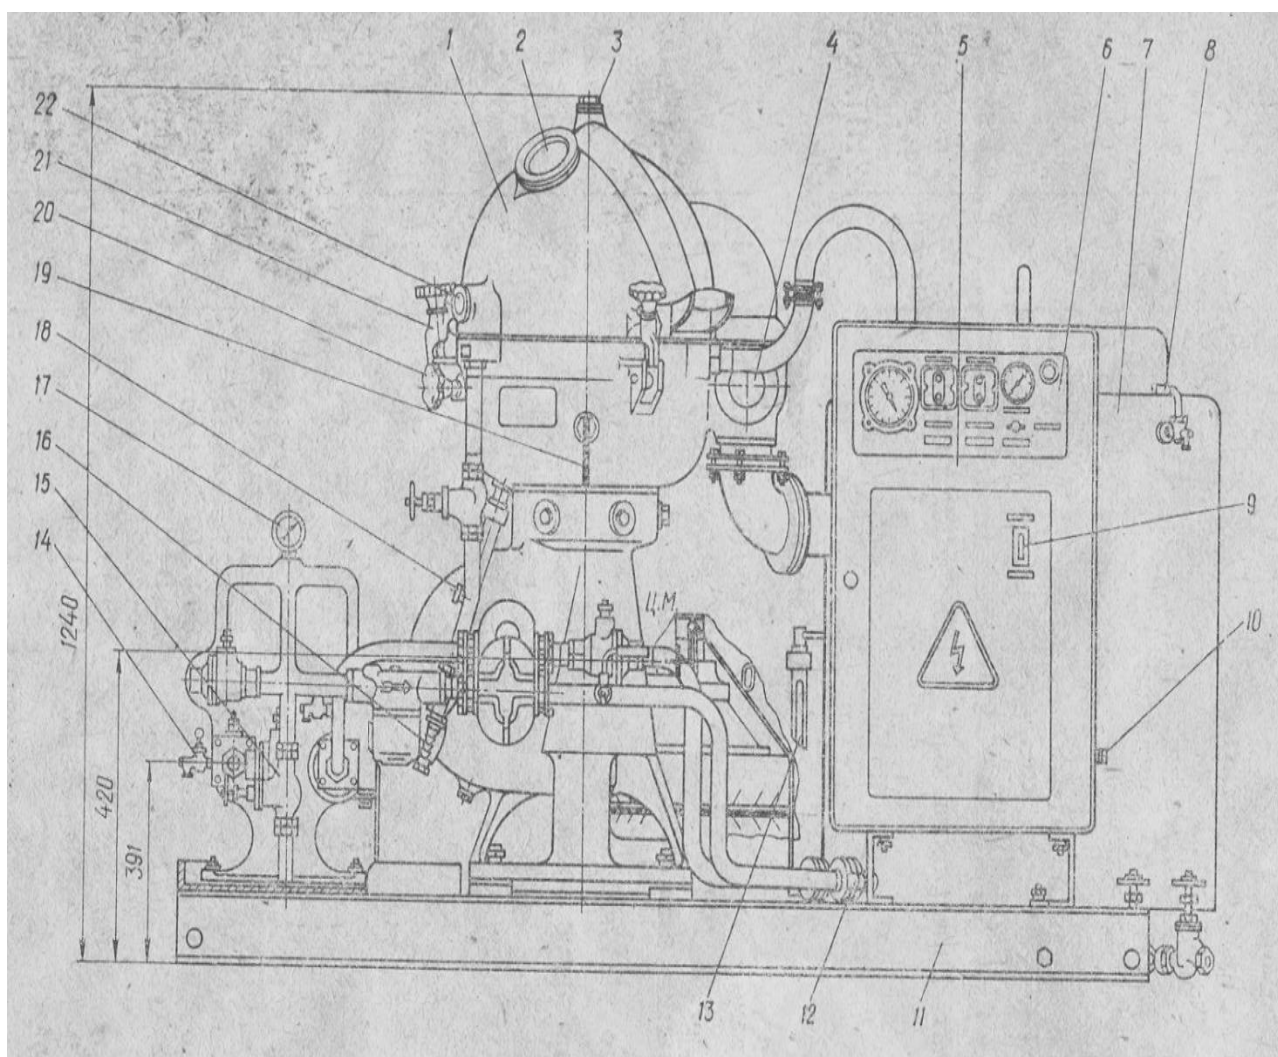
Основные узлы установки ПСМ2-4 (вид сбоку)
